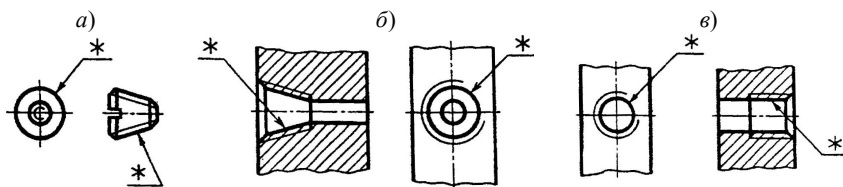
Обозначение конической и трубной цилиндрической резьбы:
